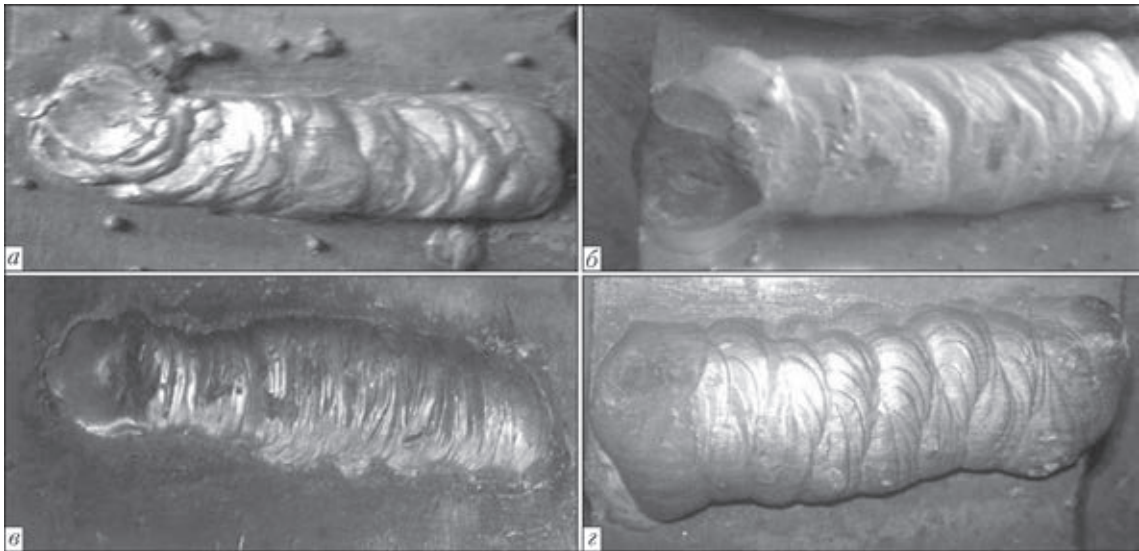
Внешний вид наплавленного металла: а — УТР-32, однослойная наплавка; б — УТР-32, трехслойная наплавка; в — электрод на Na–К стекле, однослойная наплавка; г — трехслойная наплавка электродом, изготовленном на Na–К стекле
